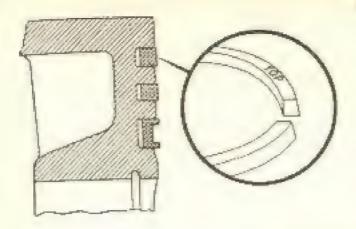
H — A marca "Top" ou "Oben" do anel de segmento superior deve ficar voltada para elma.
